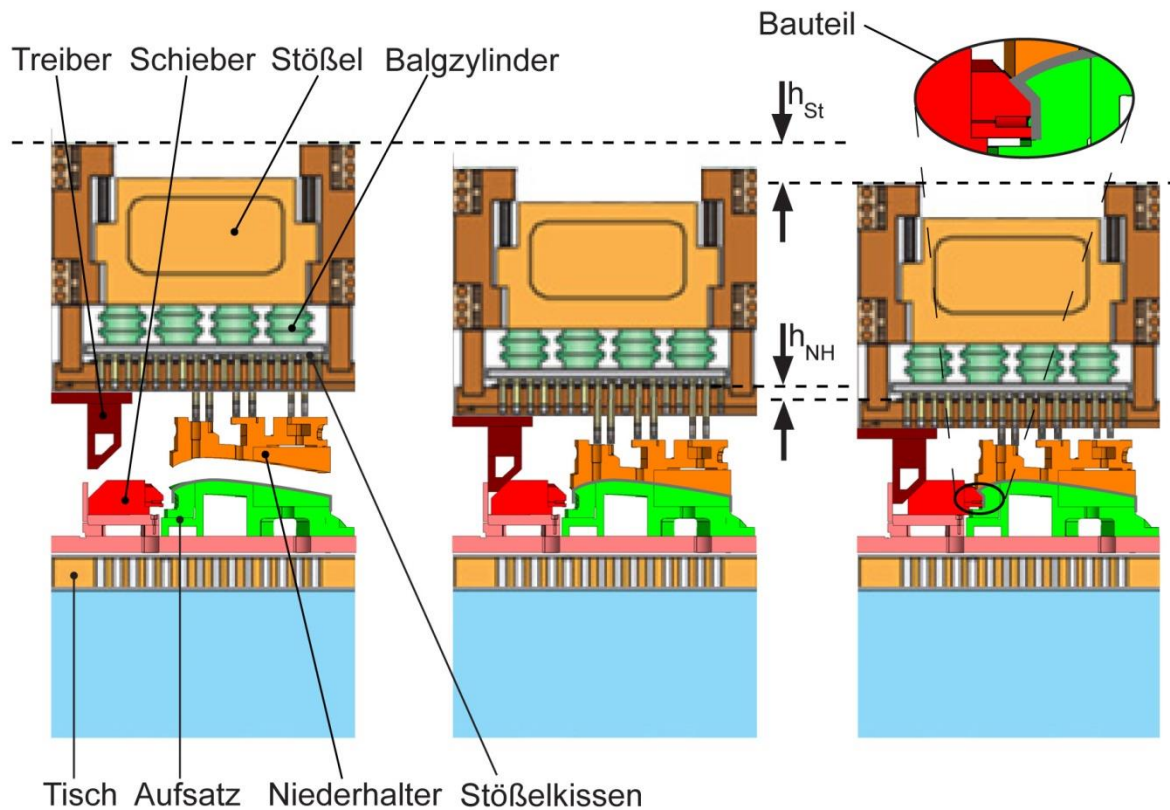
Funktionsprinzip Folgewerkzeuge mit Schieber: links geöffnetes Werkzeug, Mitte Niederhalter schließen, rechts Werkzeug in UU
